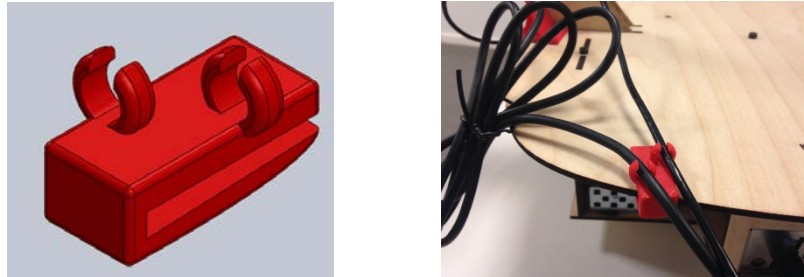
Soporte de cables, izquierda diseño modelo sólido, derecha impresión en 3D instalado en el robot.
